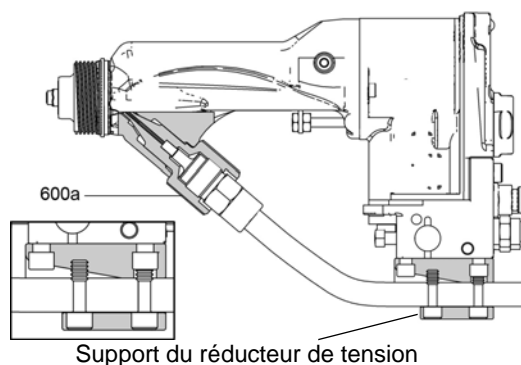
Raccordez le flexible pour fluide à base aqueuse
